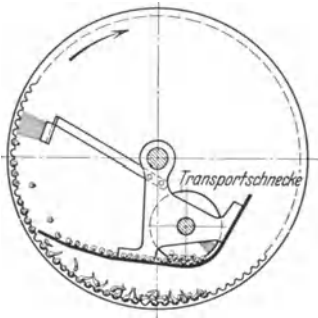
Schnittzeichnung einer Kakaokeim-Auslesemaschine.
